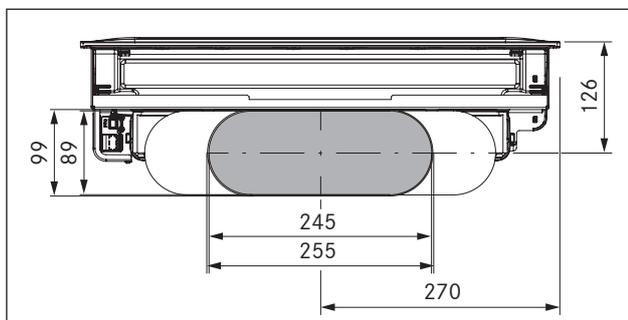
Niveau de raccordement de canaux PKA avec section droite
